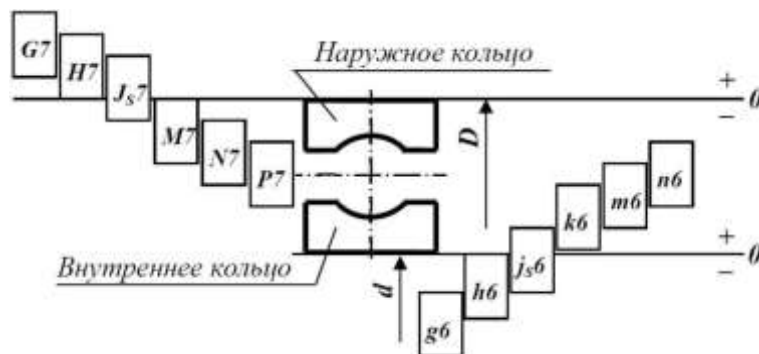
Поля допусков отверстия и вала при монтаже подшипника
